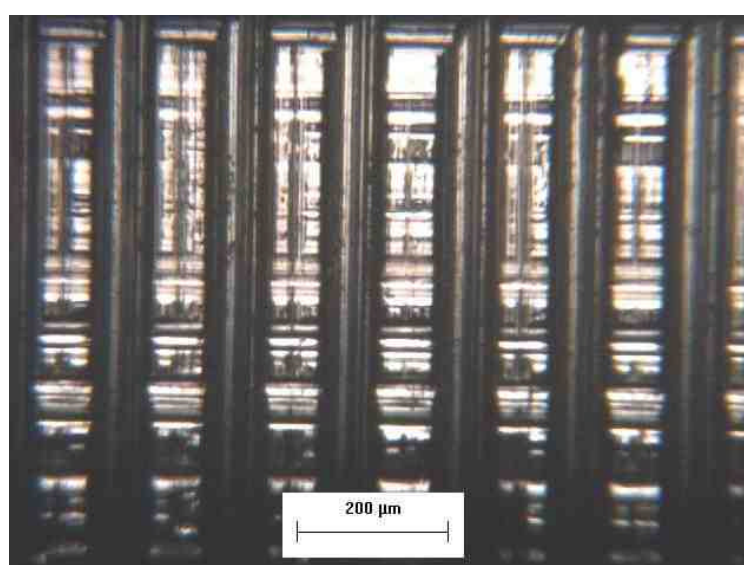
Superfície de eixo da carcaça 71 com acabamento usinado. A rugosidade média medida na superfície é de $Ra = 4,25 \text{ mm}$. (Aumento 50X).
